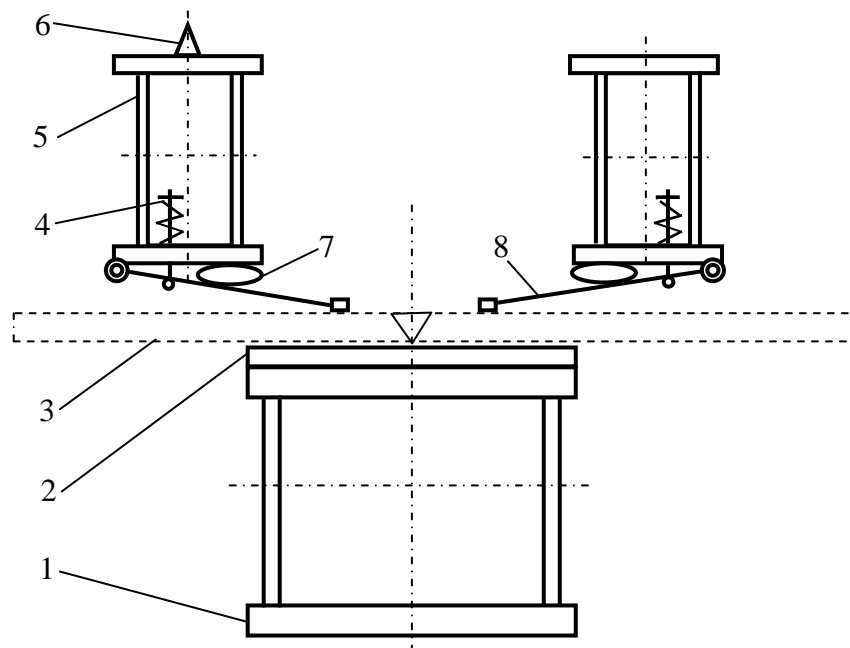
Схема стенда для складання та зварювання полотнищ: 1-нижня опорна балка; 2-підкладка; 3-зварне полотнище; 4-зворотна пружина; 5-верхня опорна балка; 6-напрямна для зварювального апарата; 7- пневмошланг; 8-притискач клавішний.
